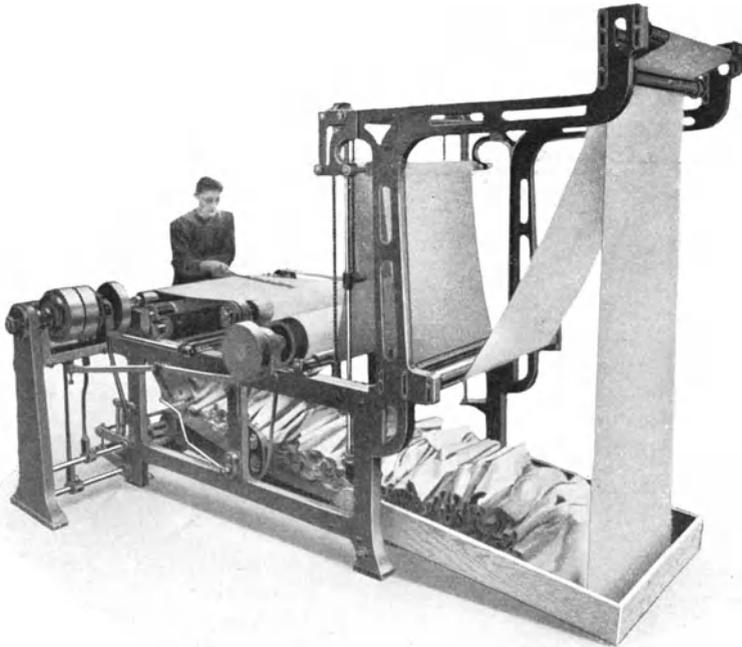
Velvetschneidmaschine mit durch Hand geführtem Messer.
